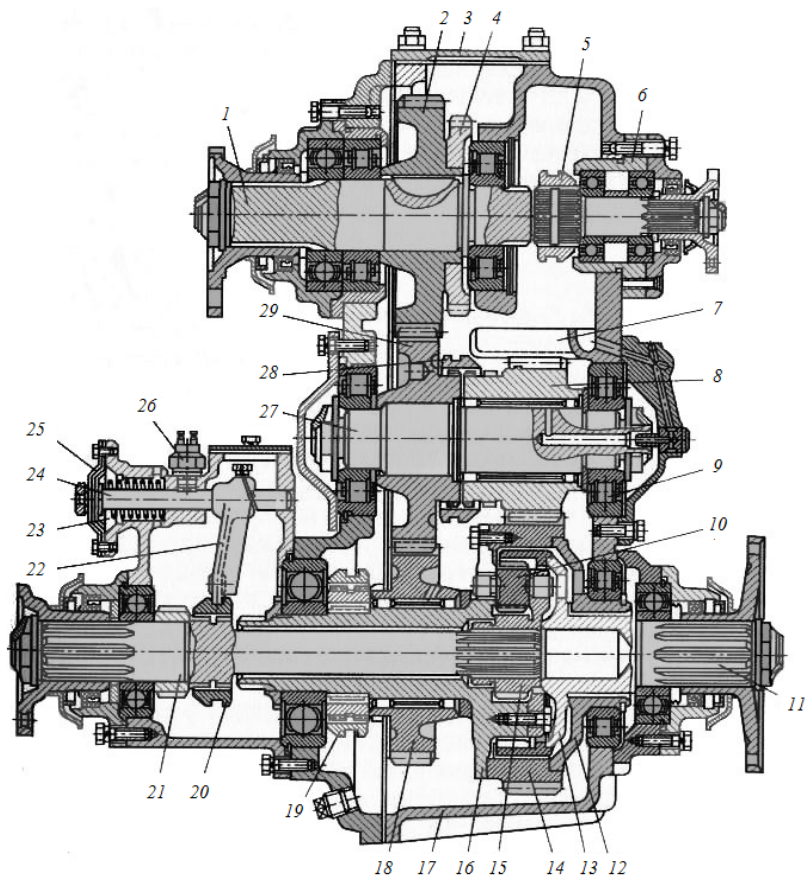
Раздаточная коробка автомобиля КамАЗ-4310: 1 – ведущий вал; 2, 14 – ведущее зубчатое колесо; 3 – крышка; 4 – зубчатое колесо; 5 – муфта включения; 6 – коробка отбора мощности на лебедку; 7 – маслосборник; 8 – промежуточная шестерня; 9 – подшипник; 10 – сателлиты; 11 – вал привода ведущих мостов; 12 – обойма дифференциала; 13 – коронное зубчатое колесо; 15 – шестерня; 16 – межосевой дифференциал; 17 – картер раздаточной коробки; 18 – шестерня повышающей передачи; 19, 20, 28 – муфта; 21 – вал привода переднего моста; 22 – вилка; 23 – пневматическая камера; 24 – шток; 25 – мембрана; 26 – электропневмоклапан; 27 – промежуточный вал; 29 – промежуточная шестерня
